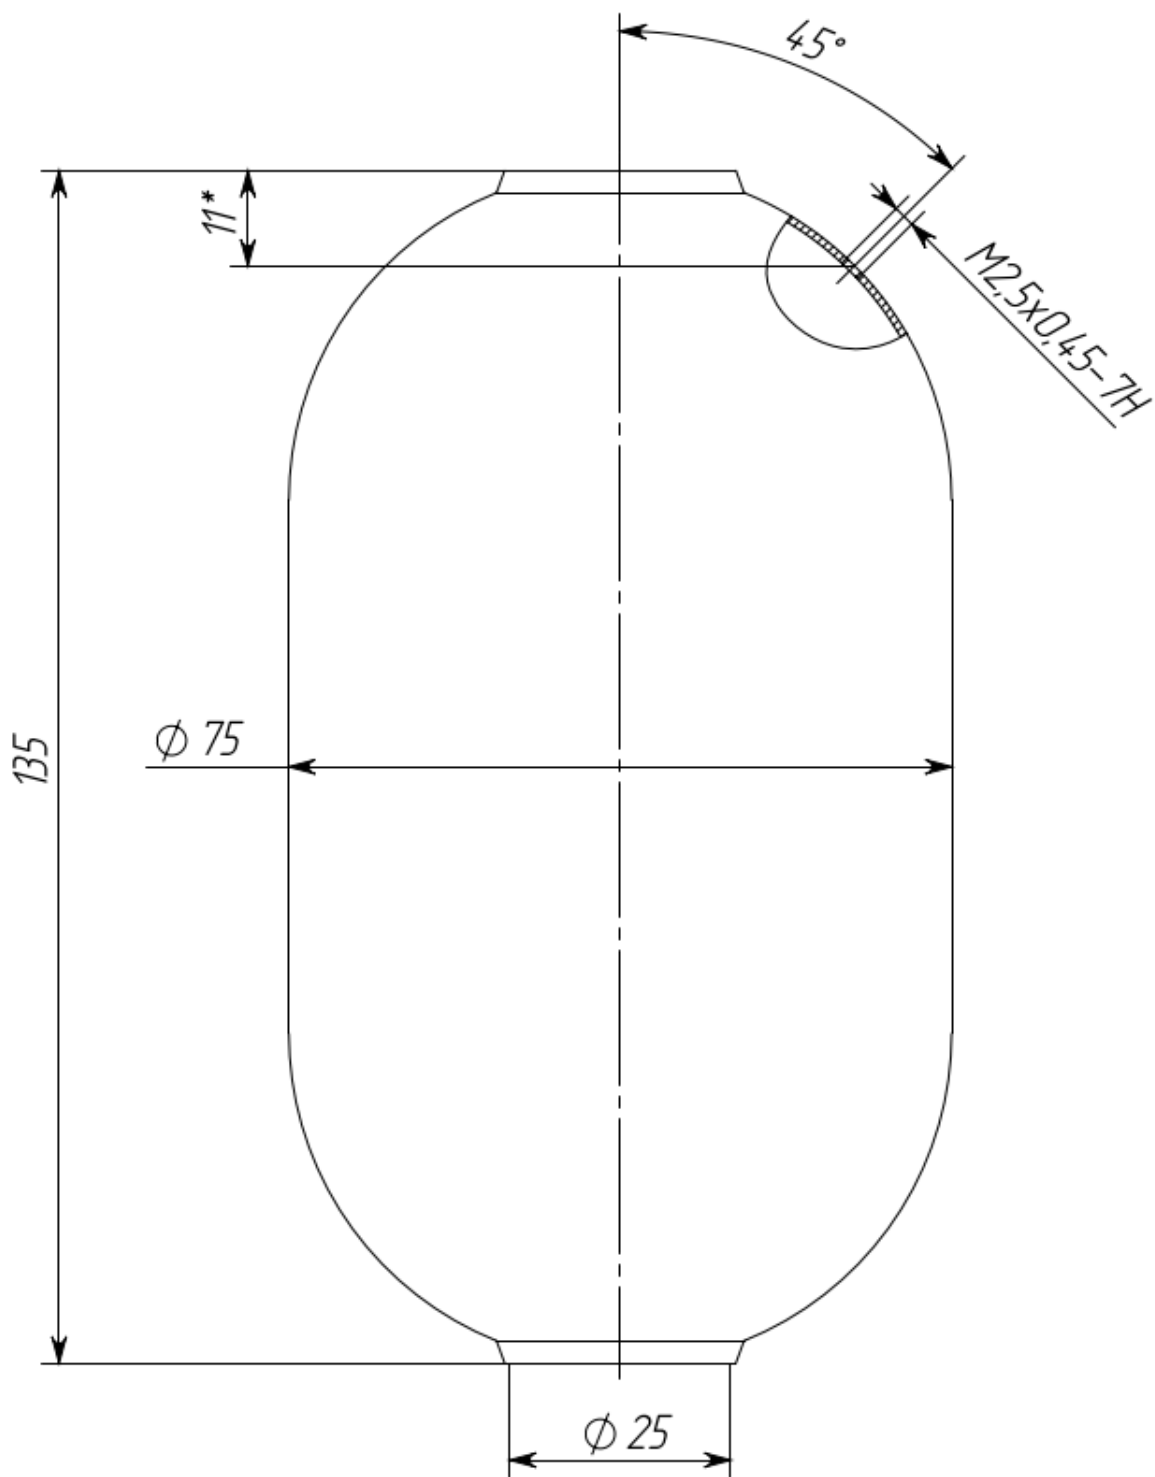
Габаритные и установочные размеры поплавка Н75
